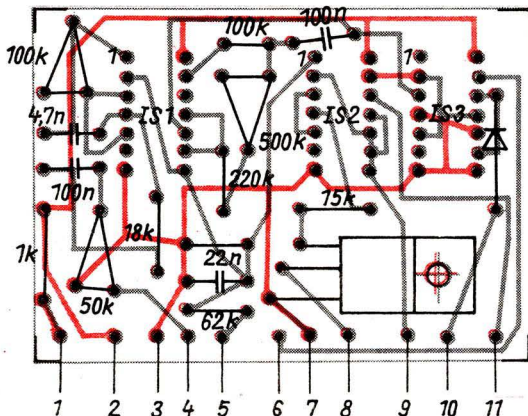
Bestückungsplan Platte 1 (Anschlußpunkte nach Tabelle 1)
